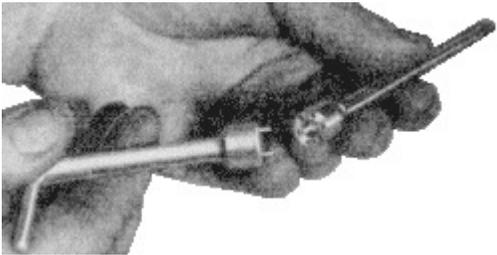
Entfernen des Kolbens mit dem Stiftschlüssel 05 MW 4-4
